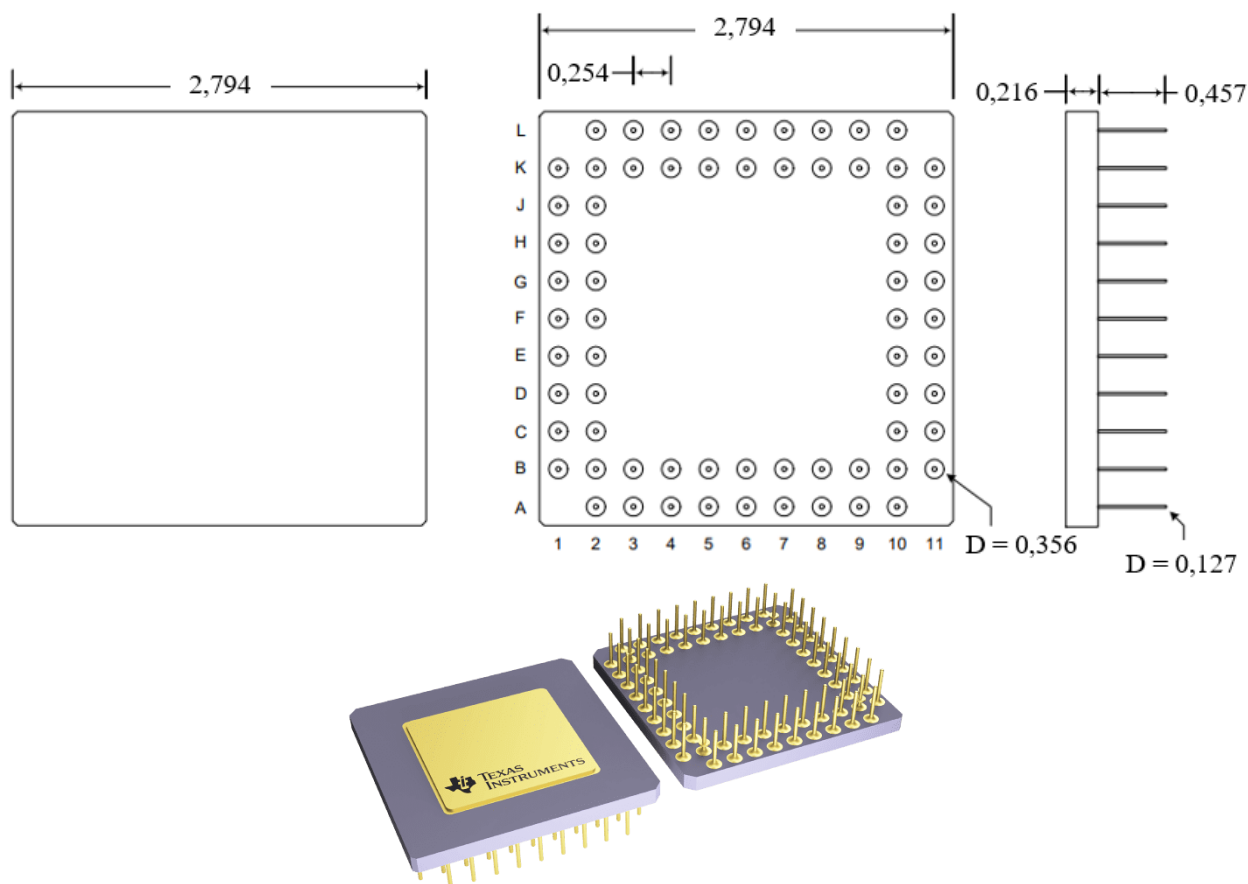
Пластиковый корпус с матрицей выводов (PGA) с 68 контактами
